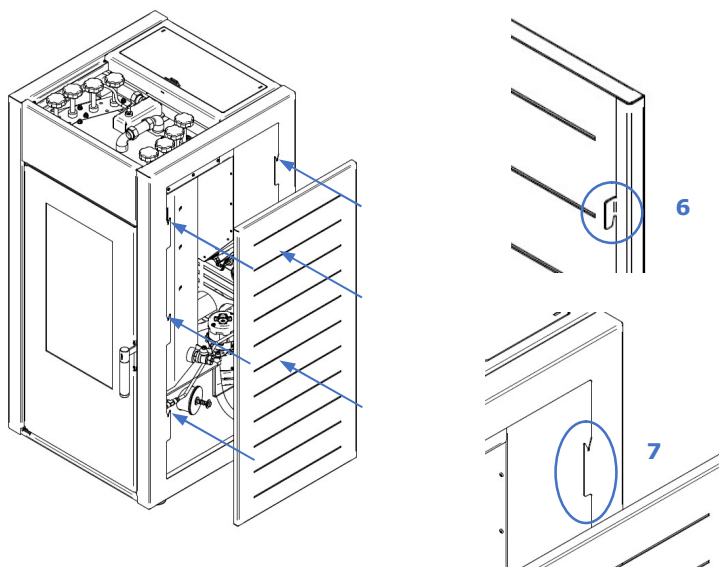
Montaje de las envolventes Hidro 17 kW y 23 kW
